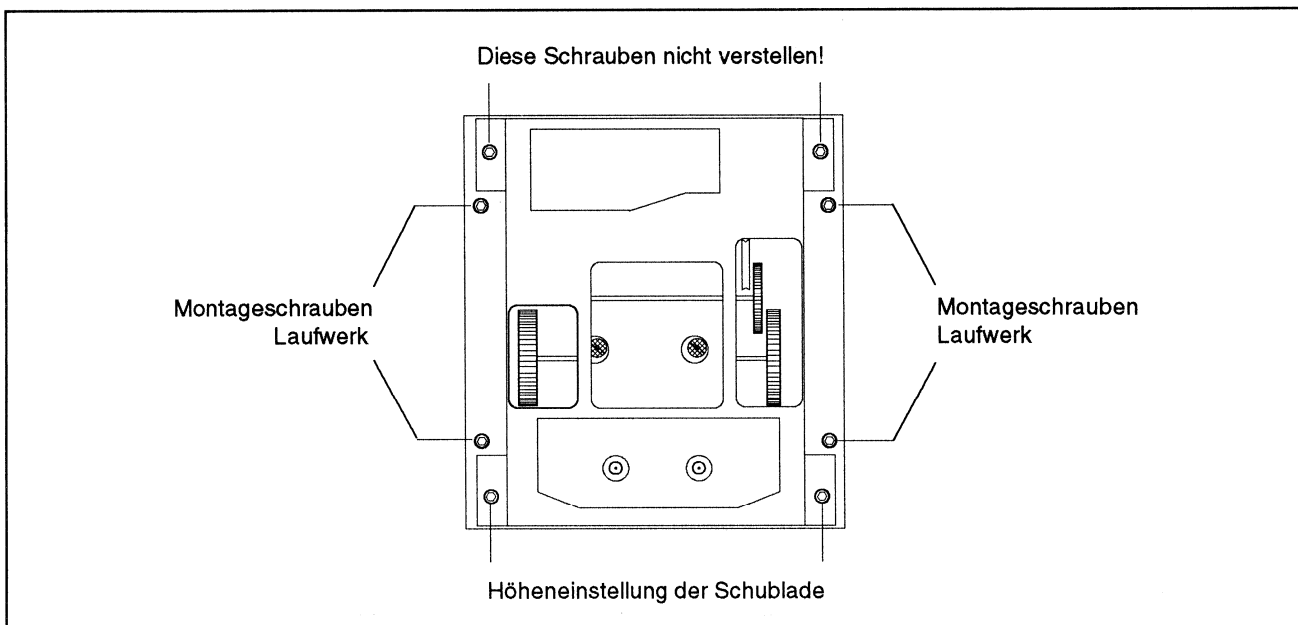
Montage- und Einstellschrauben des Laufwerks.
